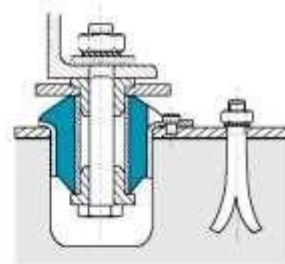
Установка между оборудованием и бетонным фундаментом (с использованием фиксирующих колец).
